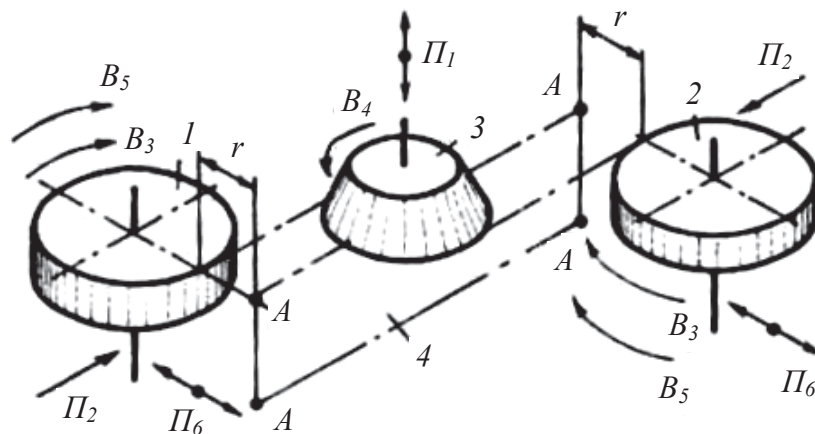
Способ долбления двух зубчатых колес при встречном движении врезания
